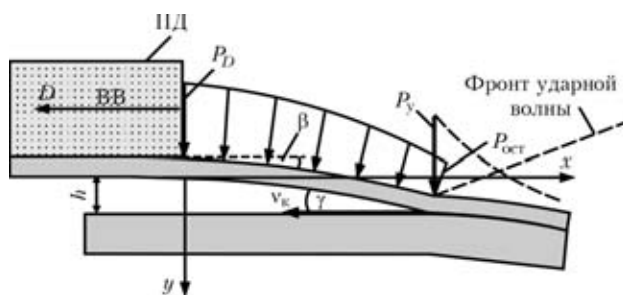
Схема сварки взрывом при параллельном расположении пластин; D — скорость детонации заряда ВВ; P_D — давление на фронте детонационной волны; h — сварочный зазор; β — угол поворота метаемой пластины; P_y — давление продуктов детонации (ПД) до соударения пластин; $P_{ост}$ — пиковое остаточное давление ПД; v_k — скорость точки контакта; γ — угол соударения
